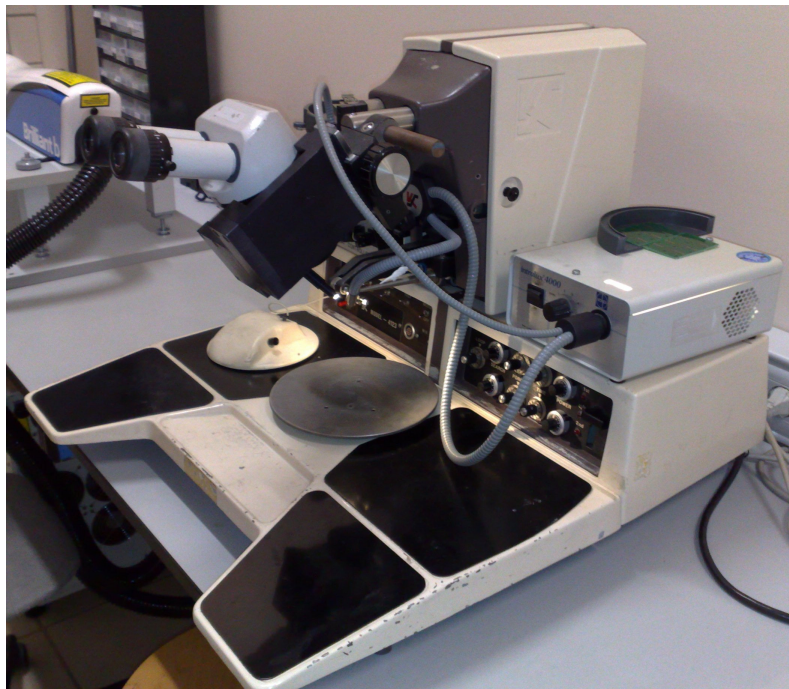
Máquina de wire bonding empleada para la soldadura de los micrhilos en las pistas de cobre.
